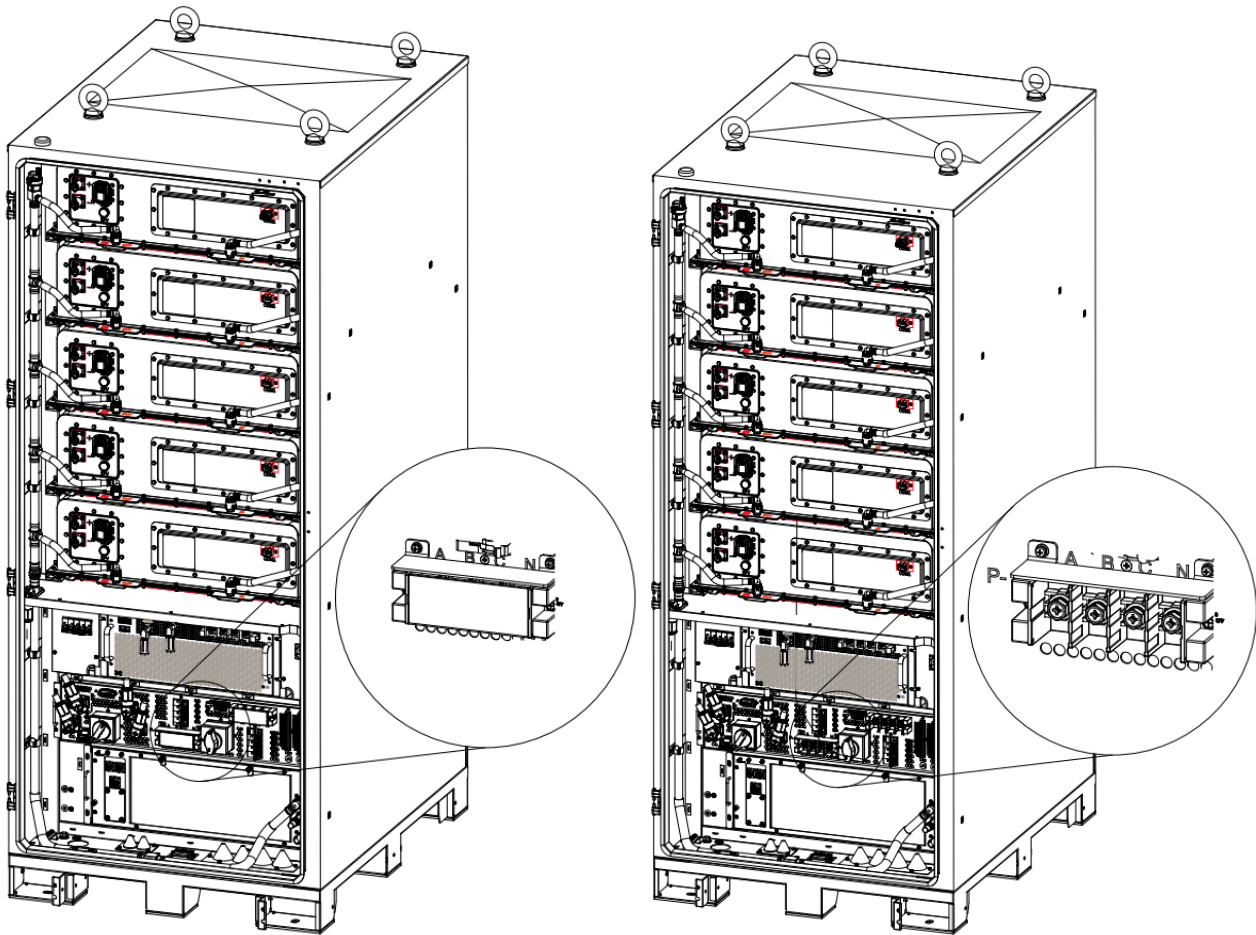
Schaltplan für den Erdungsanschluss
